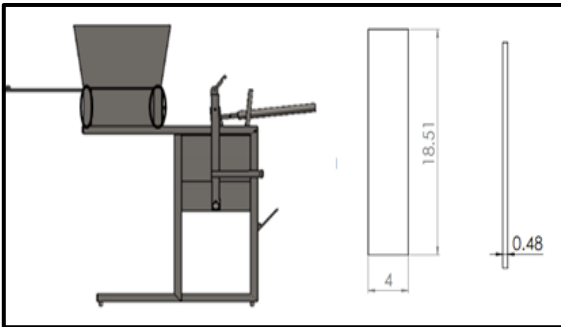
Indicación de soldadura en los apoyos, MBC-E-5-3.
